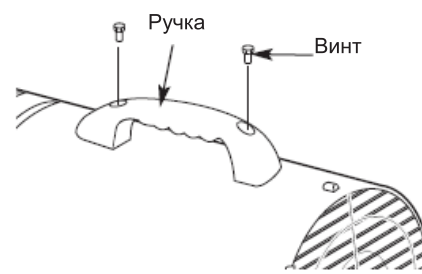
Установка ручки на модель нагревателя ТК-12000, ТК-20000
